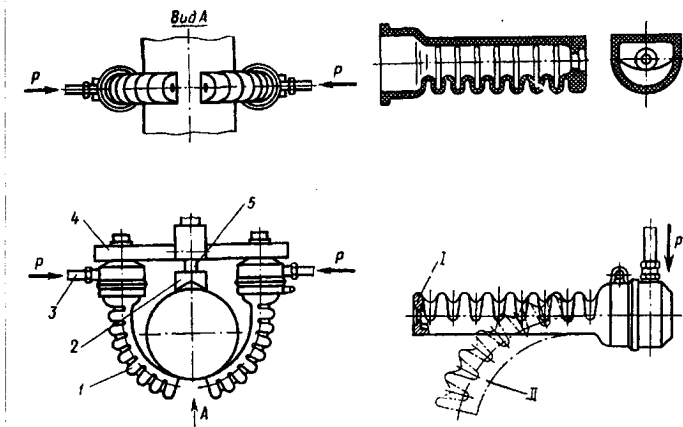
Захоплювальний пристрій з гнучкими еластичними камерами для захоплення виробів за зовнішню поверхню: 1 – еластичні камери; 2 – базуюча призма; 3 – патрубки; 4 – корпус; 5 – різьбовий утримувач; I, II – форми камери залежно від тиску стислого повітря
